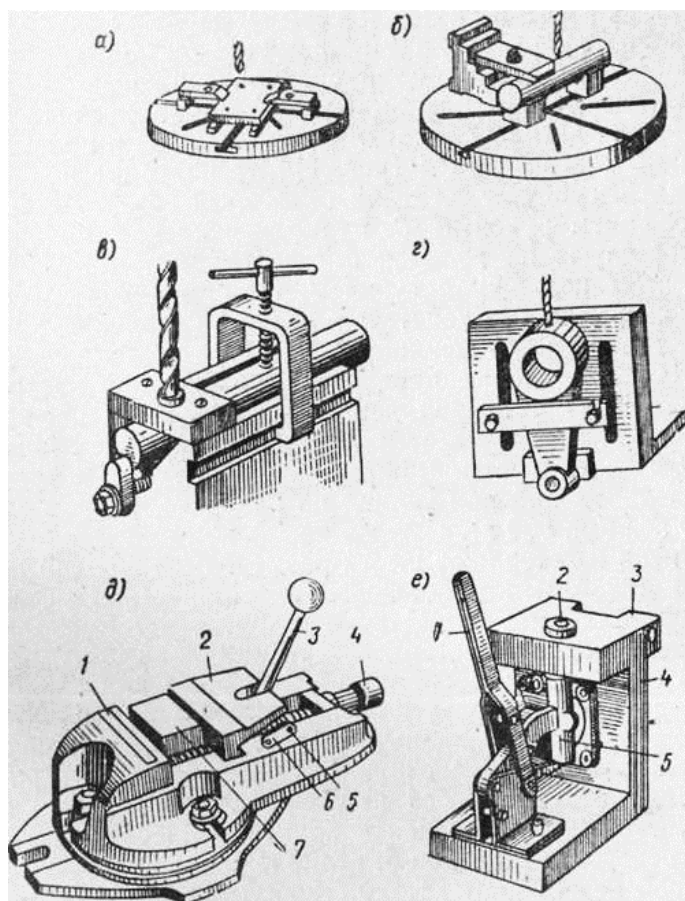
Приемы закрепления деталей при сверлении: а — на столе станка с помощью прижимных планок с бортами; б — при помощи прижимной планки и призмы; в — с помощью привмы и хомутика; г — в тисках; д — на угольнике; е — в кондукторе
